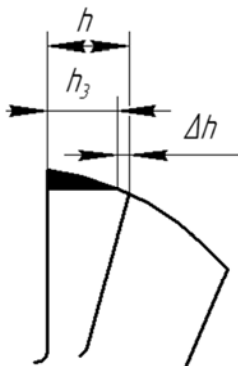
Схема износа и перетачивания зуба фрезы
